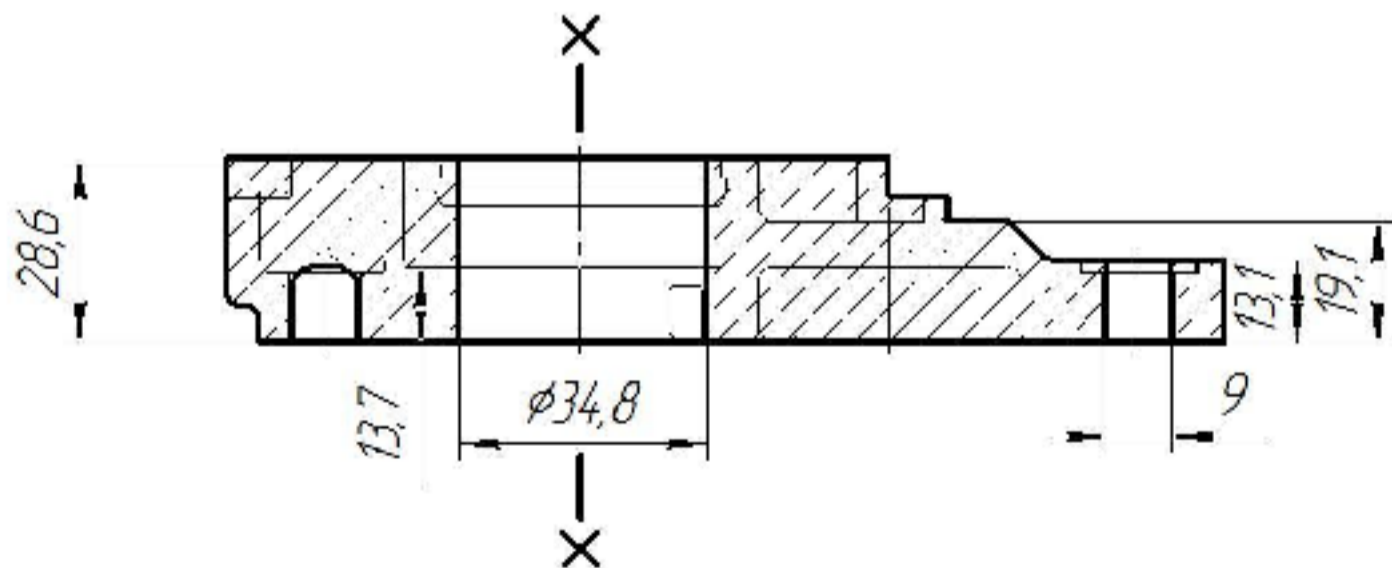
Ескіз виливків заготовок в кокіль
